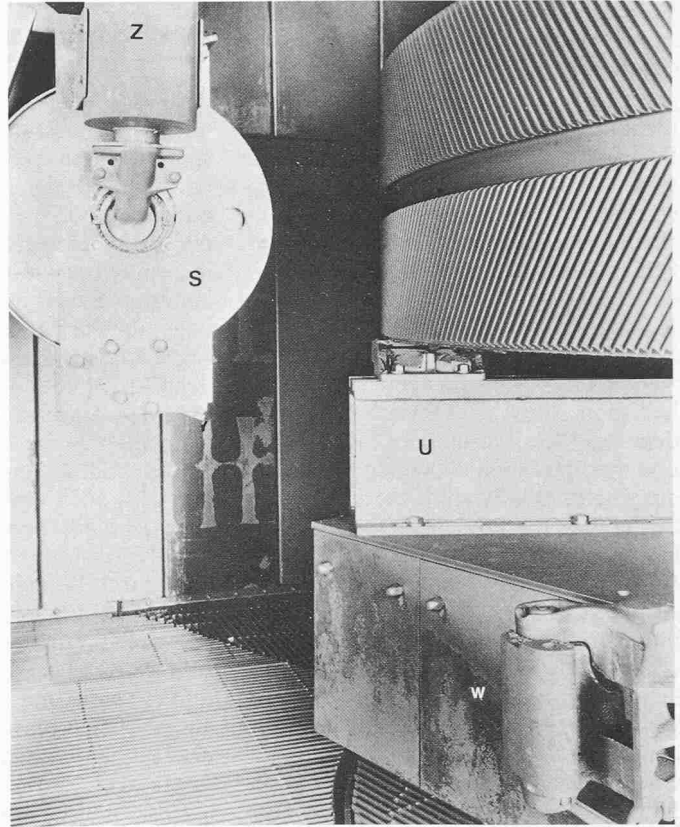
B. Mit Schleuderrad ausgerüstete, amerikanische Anlage zum Peenen grosser Zahnräder mit bis zu 5 Meter Durchmesser. Detail der Anlage Bild 28A. Das im Hintergrund zu sehende Schleuderrad führt während der Peening-Behandlung eine vertikale hin- und hergehende Bewegung aus.
